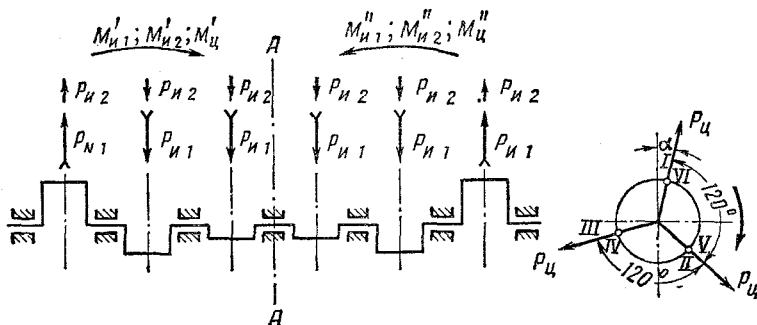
Схема направления сил инерции в шестицилиндровом двигателе, колена коленчатого вала которого расположены под углом  $120^\circ$ .
